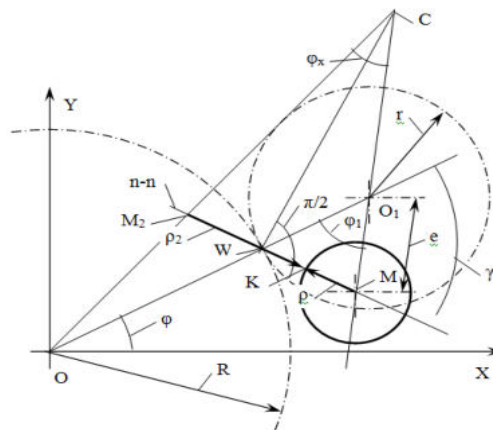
Схема к вычислению координат профиля зубьев колеса
